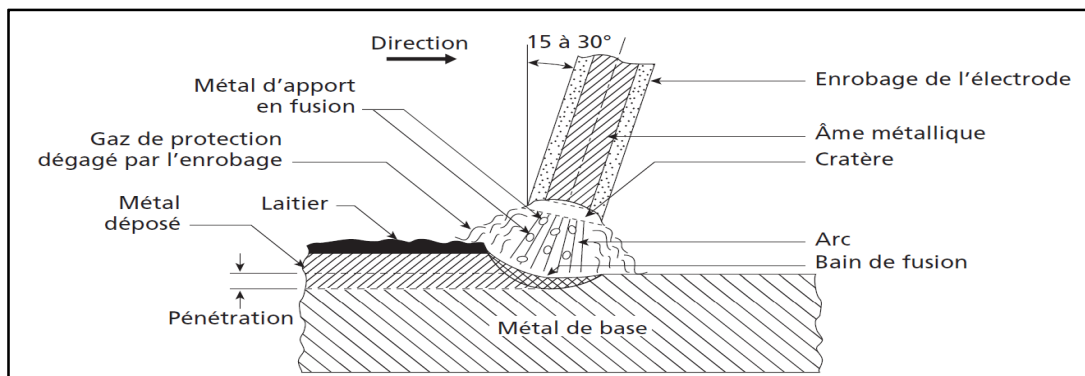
Principe de soudage à l'arc avec électrode enrobée (SMAW) [12]
